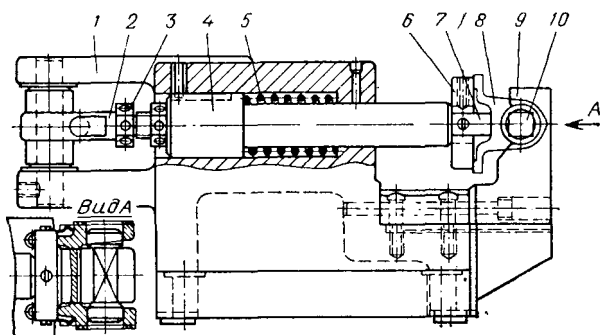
Приспособление для протягивания наружных плоскостей вилок
